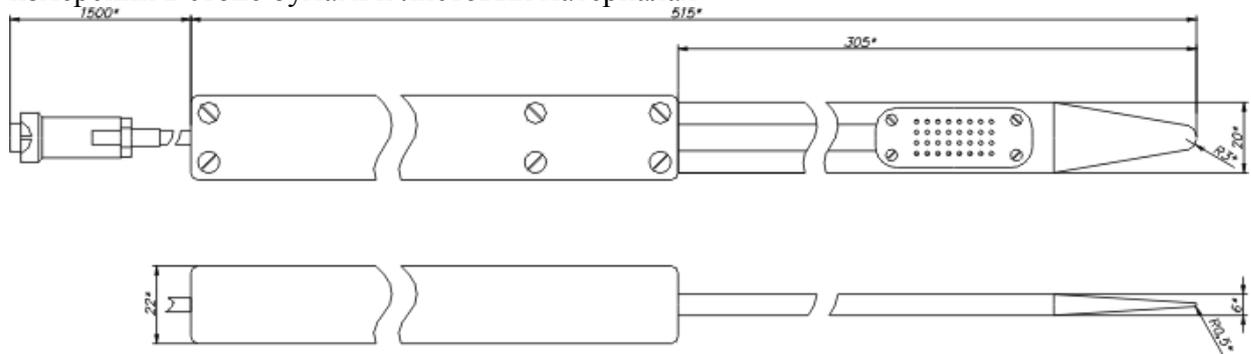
Измерительный преобразователь ИПВТ-03-11-ПВ
